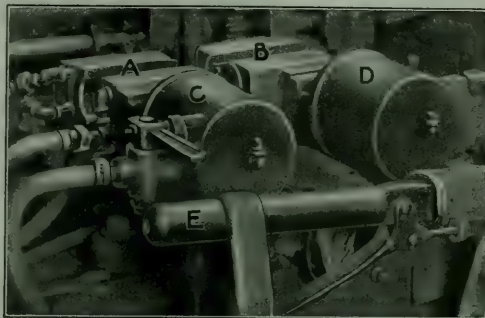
A. MÁQUINA PARA SOLDAR LOS EXTREMOS DE LOS TUBOS
